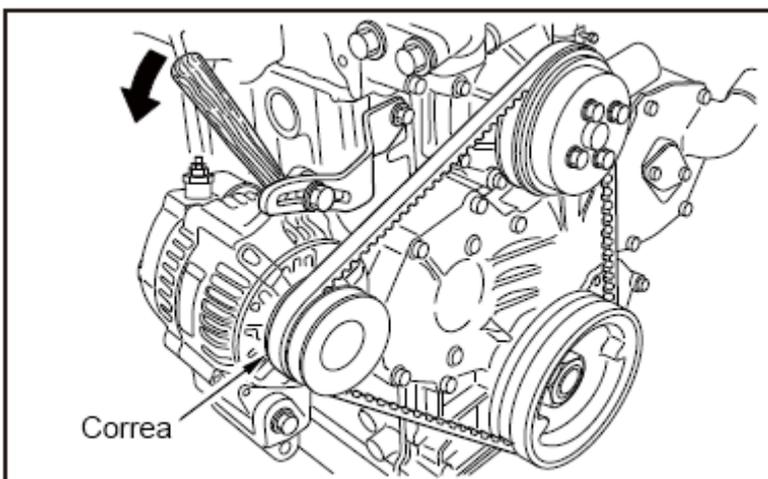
Correa y tensión de la correa - Inspección y Ajuste
